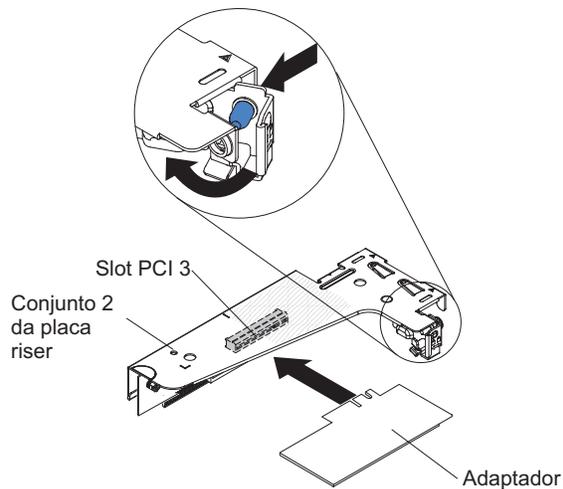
Instalação do Adaptador no Conjunto da Placa Riser PCI 2
